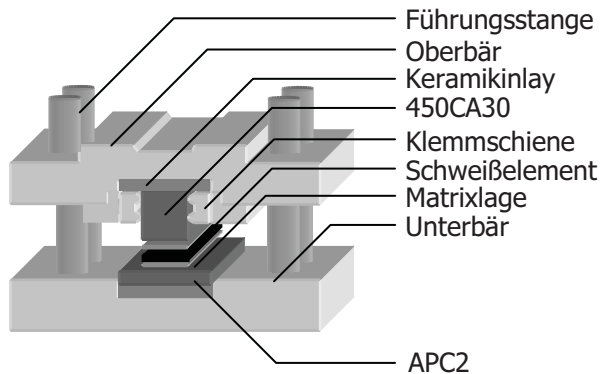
Explosionszeichnung des Kurzfaser-Werkzeugs
